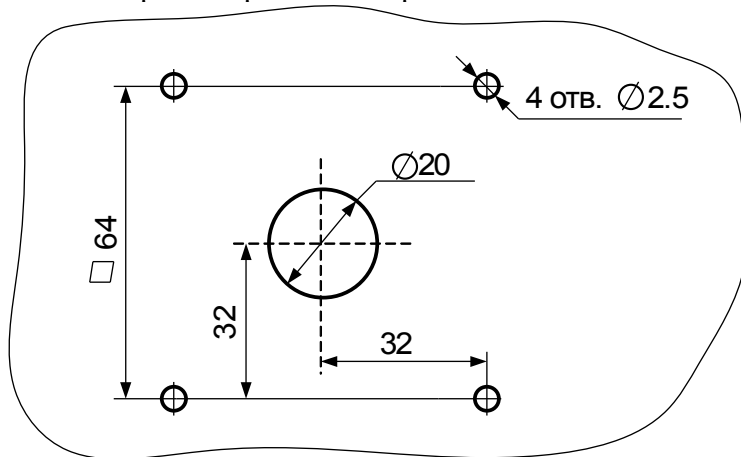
Чертеж разметки на баке для сверления отверстий для установки датчика ДУ-02М.
